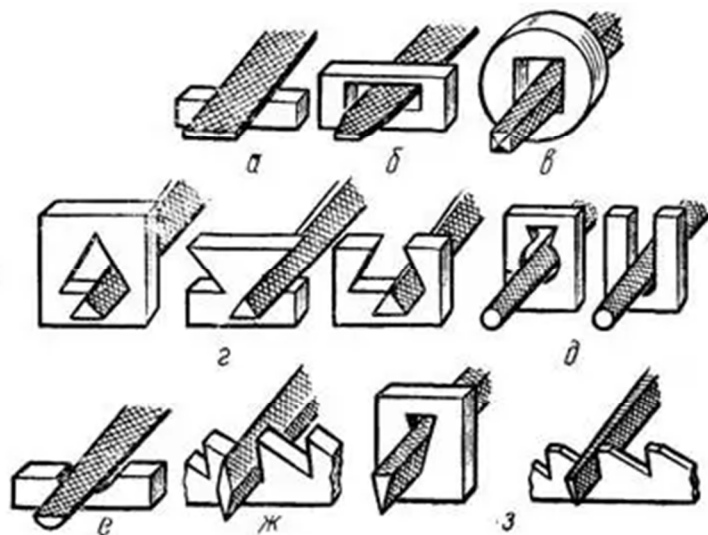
Формы сечений напильников: а и б — плоские; в — квадратный; г — трехгранный; д — круглые; е — полукруглый; ж — ромбический; з — ножовочные.
